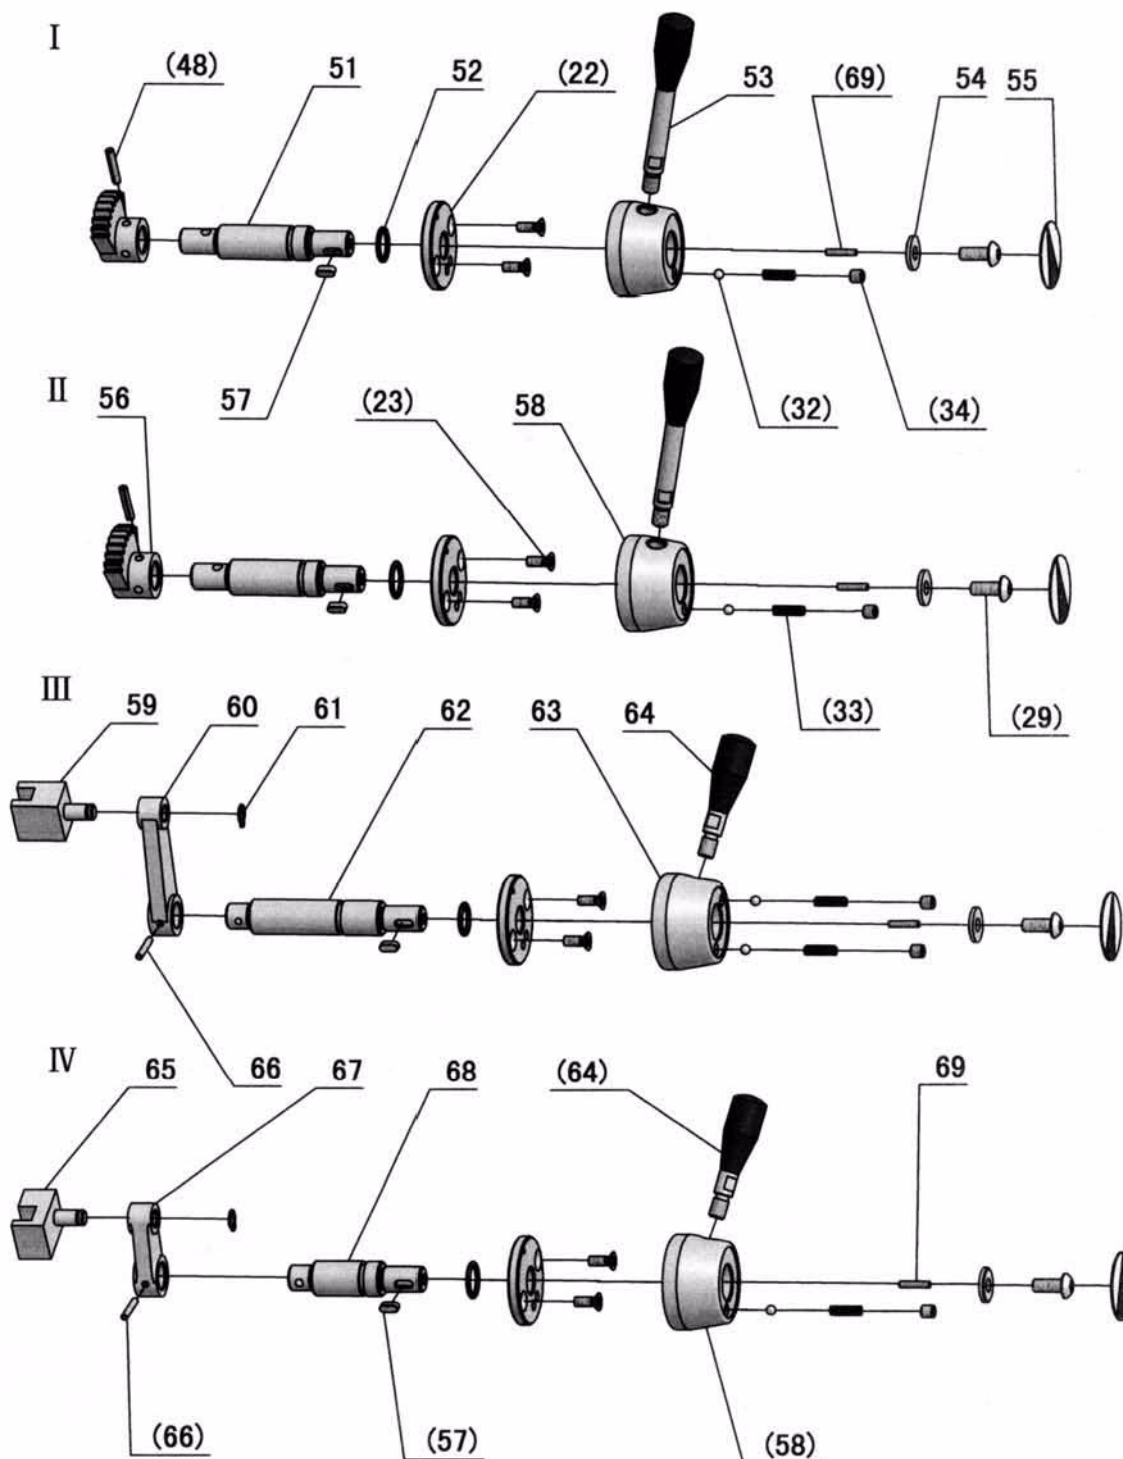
Spindelstock 2 von 8 - Headstock 2 of 8
